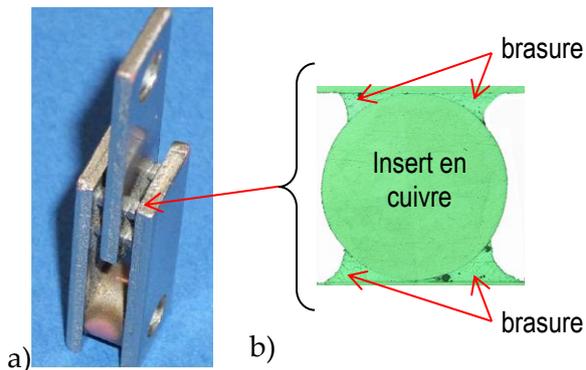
Éprouvettes de caractérisation de brasure en configuration bump, (b) vue en coupe d'un bump
